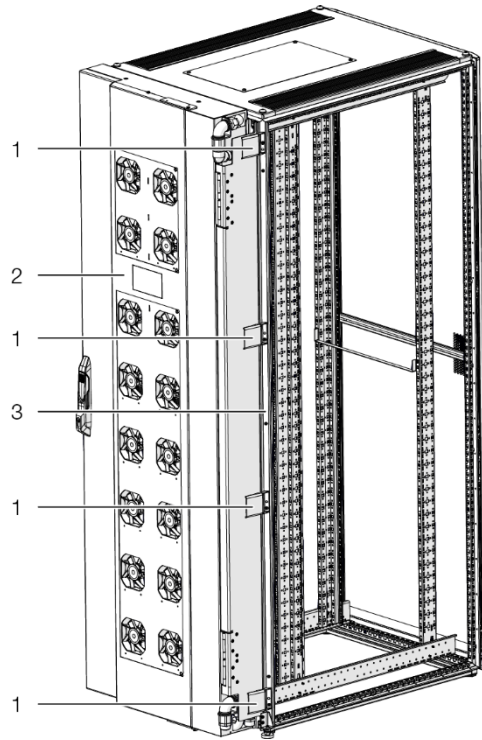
Zarge mit vier Befestigungsbohrungen des LCP Rear Door CW
